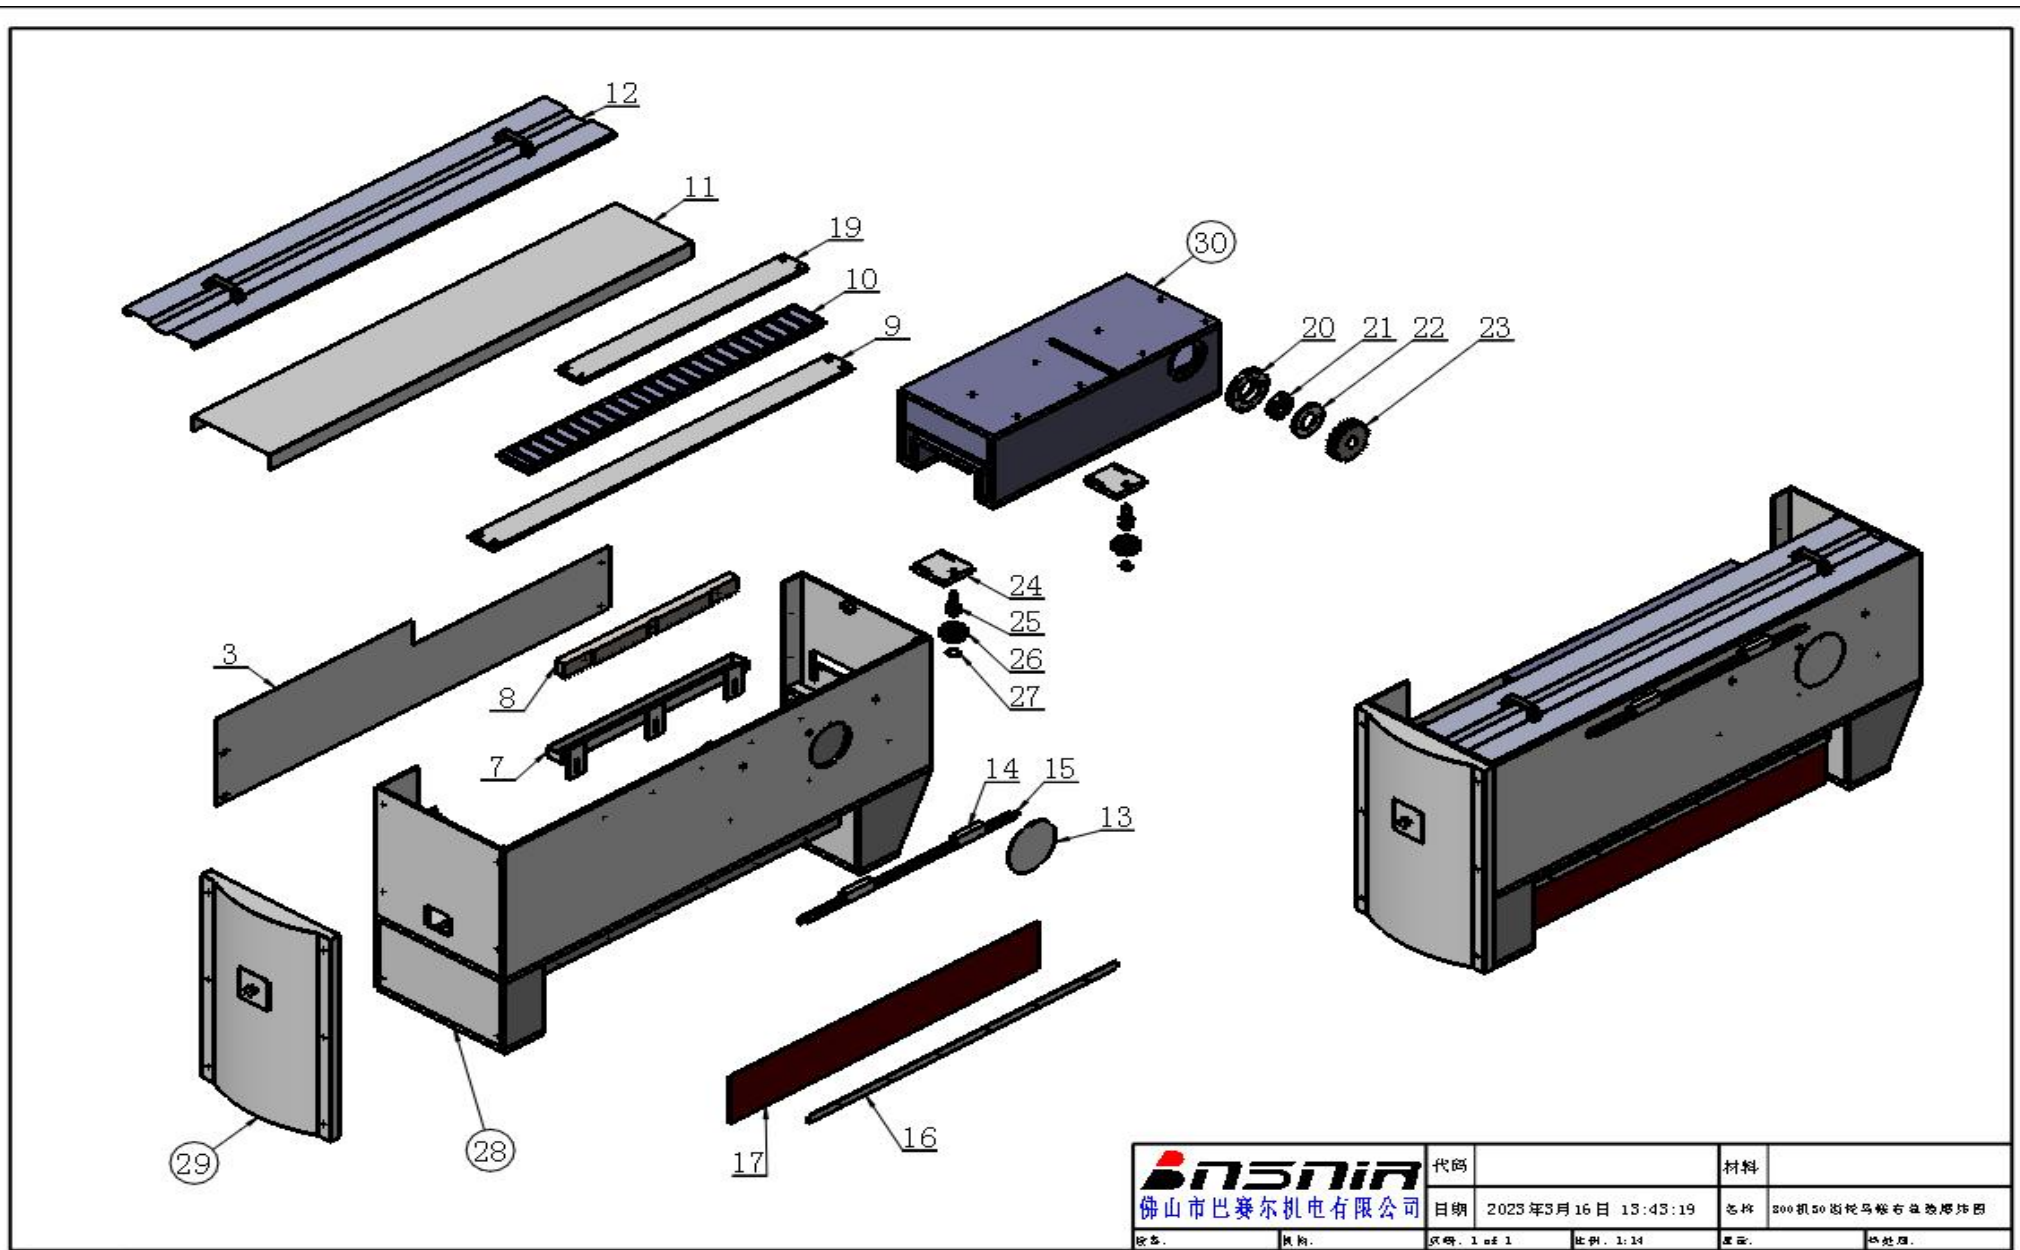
2 BP1000/16 抛光机——马鞍(右)装配图 picture 3-2 Assembly drawing of BP1000/16 polishing machine -- saddle (right)
